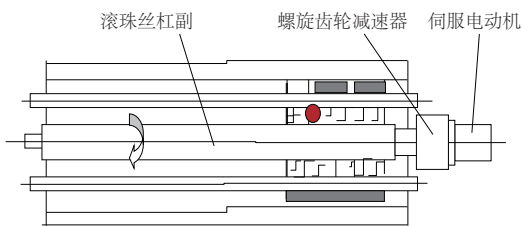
滚珠丝杠与螺旋齿轮复合传动减速器
